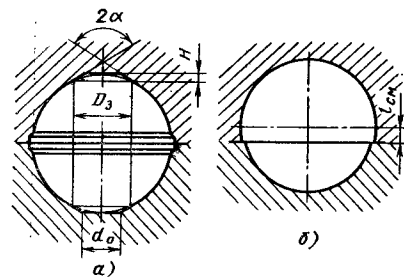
Схемы малооблойной штамповки заготовок шариков:
